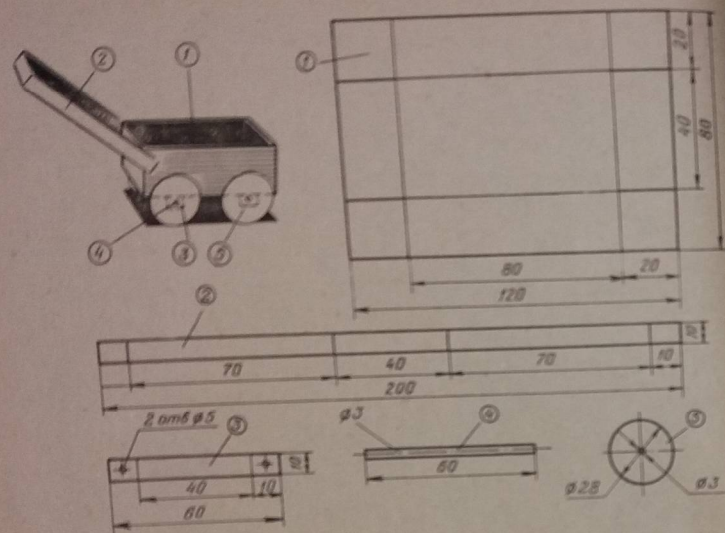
Модель тележки: 1—корпус; 2—ручка; 3—подшипник; 4—ось; 5—колесо
